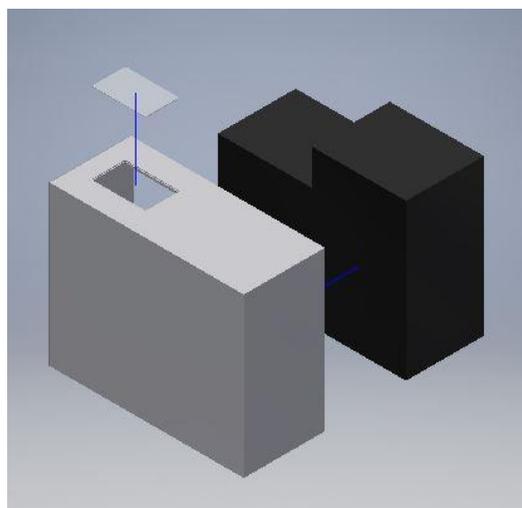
Explosionado del mueble caja del Pop Up
